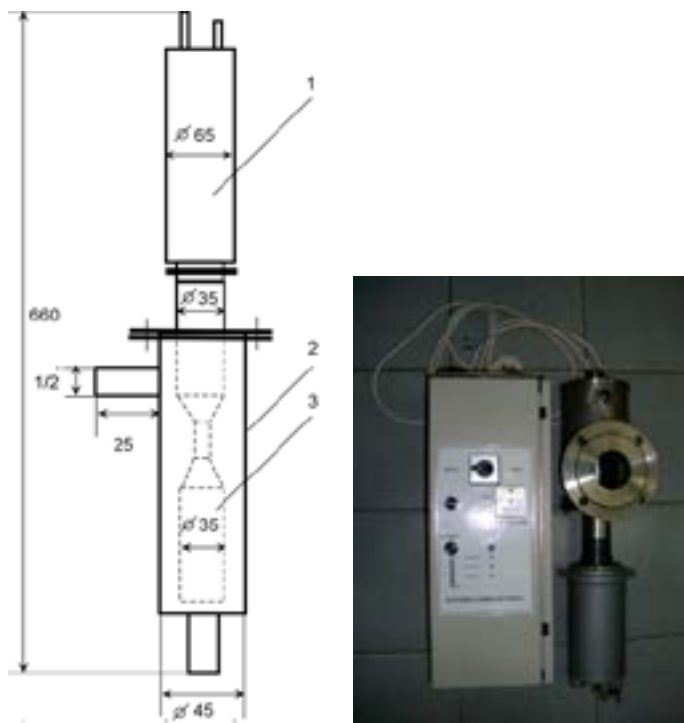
Конструкционная схема и общий вид проточного сонохимического реактора
